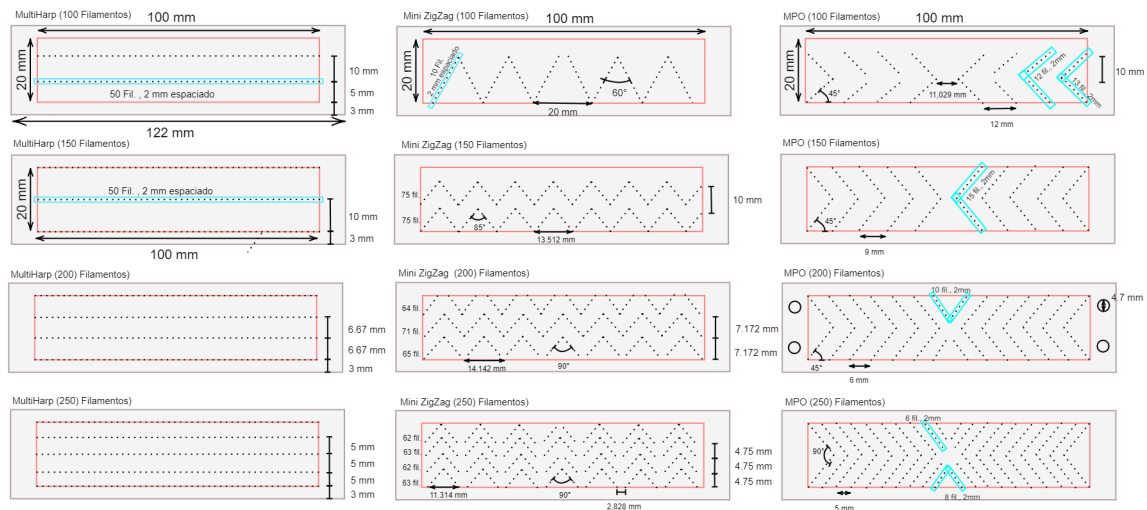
Esquemas detallados de vista en planta de prototipos MH, MZZ y MPO para distinto número de filamentos.
